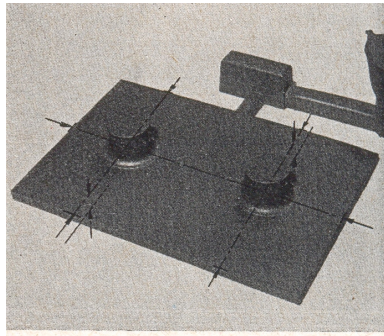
Corpo de prova de placa sobre bossas. Dimensões da placa: 152 mm x 254 mm x 8 mm. Dimensões das bossas: \varnothing 32 mm x 25 mm (29).
